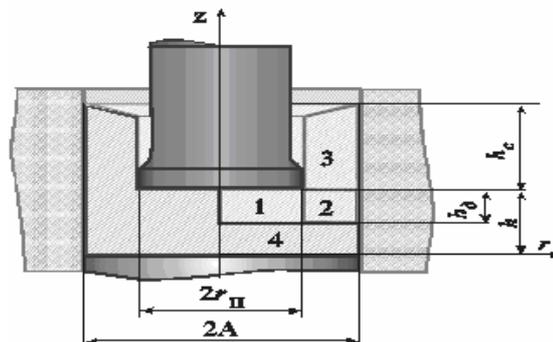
Схема выдавливания детали и разбивка заготовки на зоны
